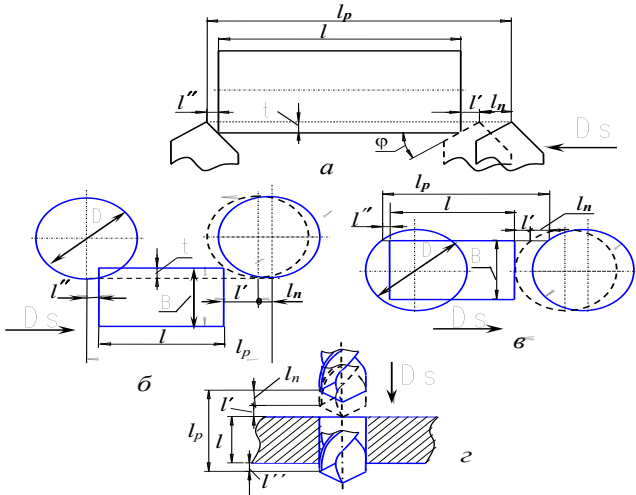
Схеми для визначення робочого ходу інструменту під час точіння (а), циліндричного (б) і чорнового (в) торцевого фрезерування та свердління (г)
